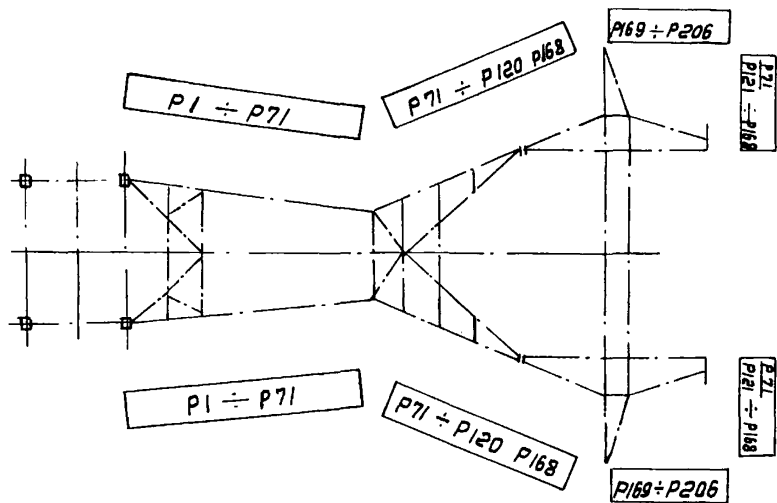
План расположения пакетов с деталями аппар. P1 или P2
